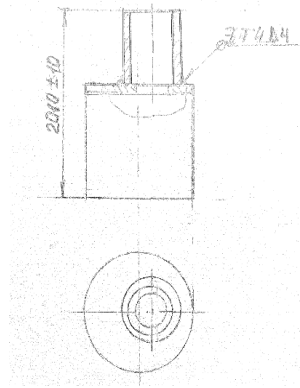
Эскиз сварки корпуса и горловины
